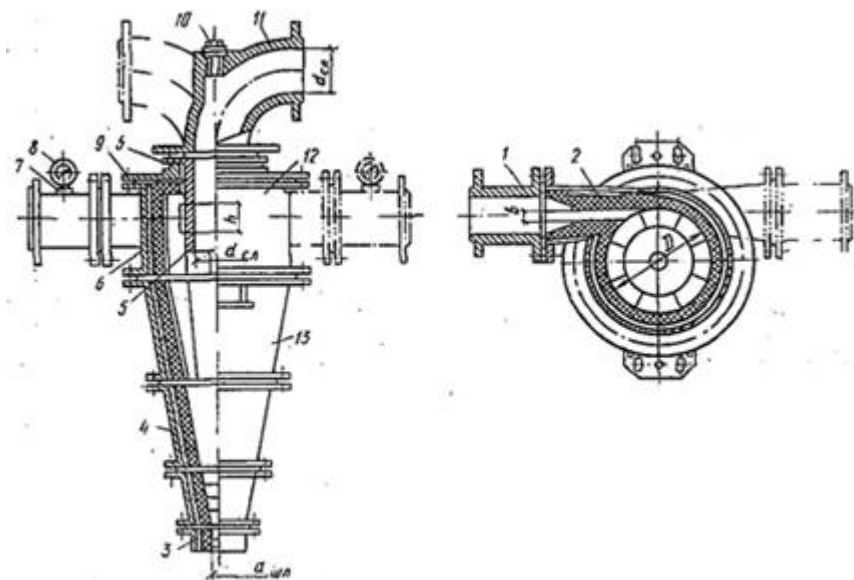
Напорный гидроциклон: 1 — питающий патрубок; 2 — съемный, резиновый вкладыш; 3 — шламовый патрубок; 4 — составные элементы конической части; 5 — сливной патрубок; 6 — цементная стяжка; 7 — мембранный разделитель; 8 — манометр; 9 — крышка цилиндрической части; 10 — заглушка отверстия для подключения импульсной линии системы автоматического регулирования гидроциклона; 11 — внешний сливной патрубок; 12 — цилиндрическая часть; 13 — коническая часть.
